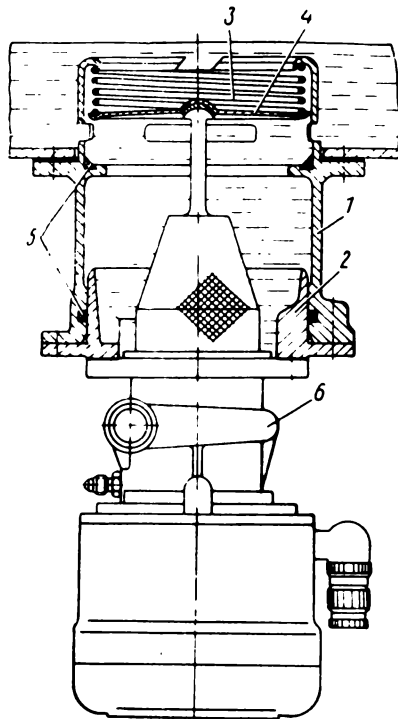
Монтажное устройство для монтажа и демонтажа внебаковых насосных агрегатов без слива топлива из баков:
